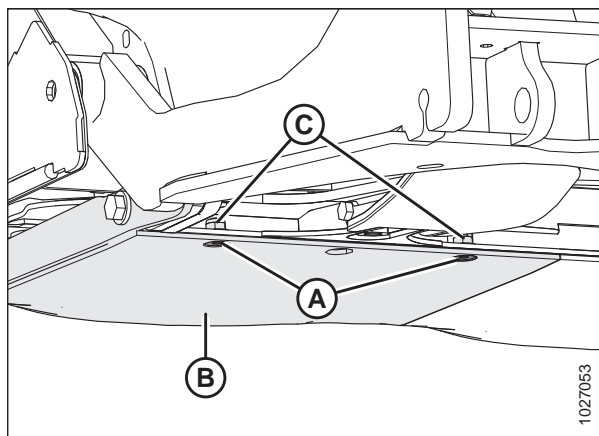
Левый наружный защитный палец – Вид сзади
